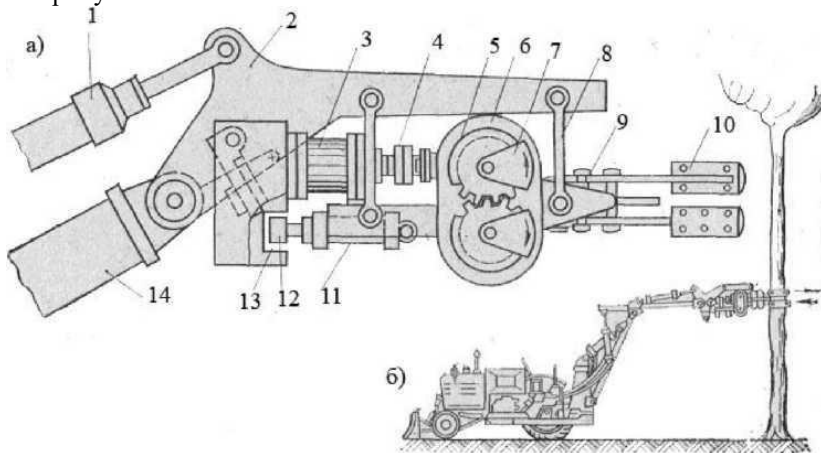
Схема вібраційної установки «Кедрівка»: а) принципова схема установки: 1 - гідроциліндр; 2 - корпус вібратора; 3 - гідромотор; 4 - пружна муфта; 5 - циліндрична шестірня; 6 - двоступінчастий редуктор; 7 - дебаланс; 8 - пружна підвіска; 9 - гідроциліндр; 10 - захватна лапа; 11 - гідроциліндр для фіксування вібратора в транспортне положення; 12 - клиновий замок; 13 - упорна п'ята; 14 - шарнірна стріла; б) одна з модифікацій віброустановки «Кедрівка» – «Кедрівка-Е», монтується на базі екскаватора Е-153А (Е-2515) після демонтажу екскаваторного ковша.
